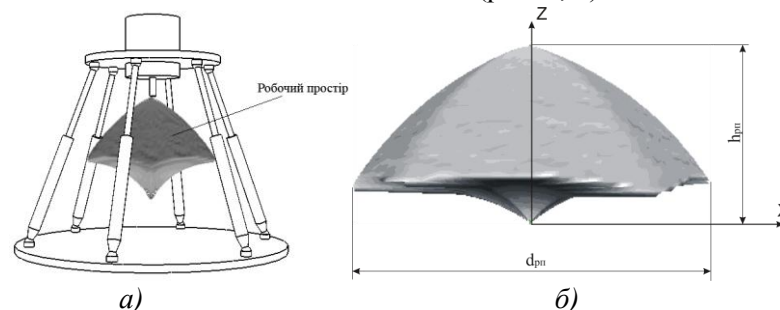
Робочий простір верстата-гексапода: а) розташування; б) параметри
